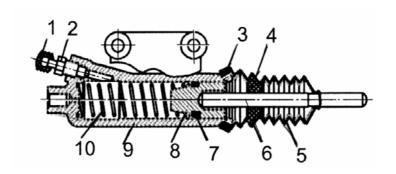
Рабочий цилиндр привода выключения сцепления:
